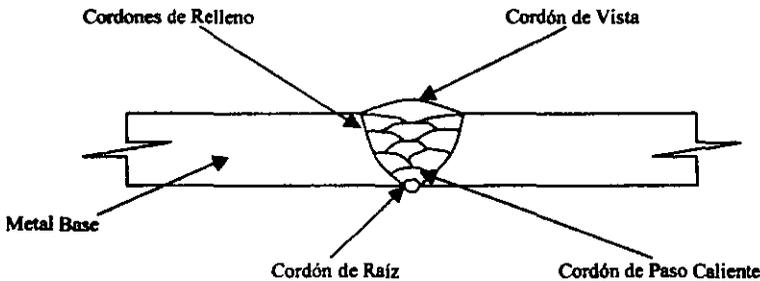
Identificación de los Cordones de Soldadura
